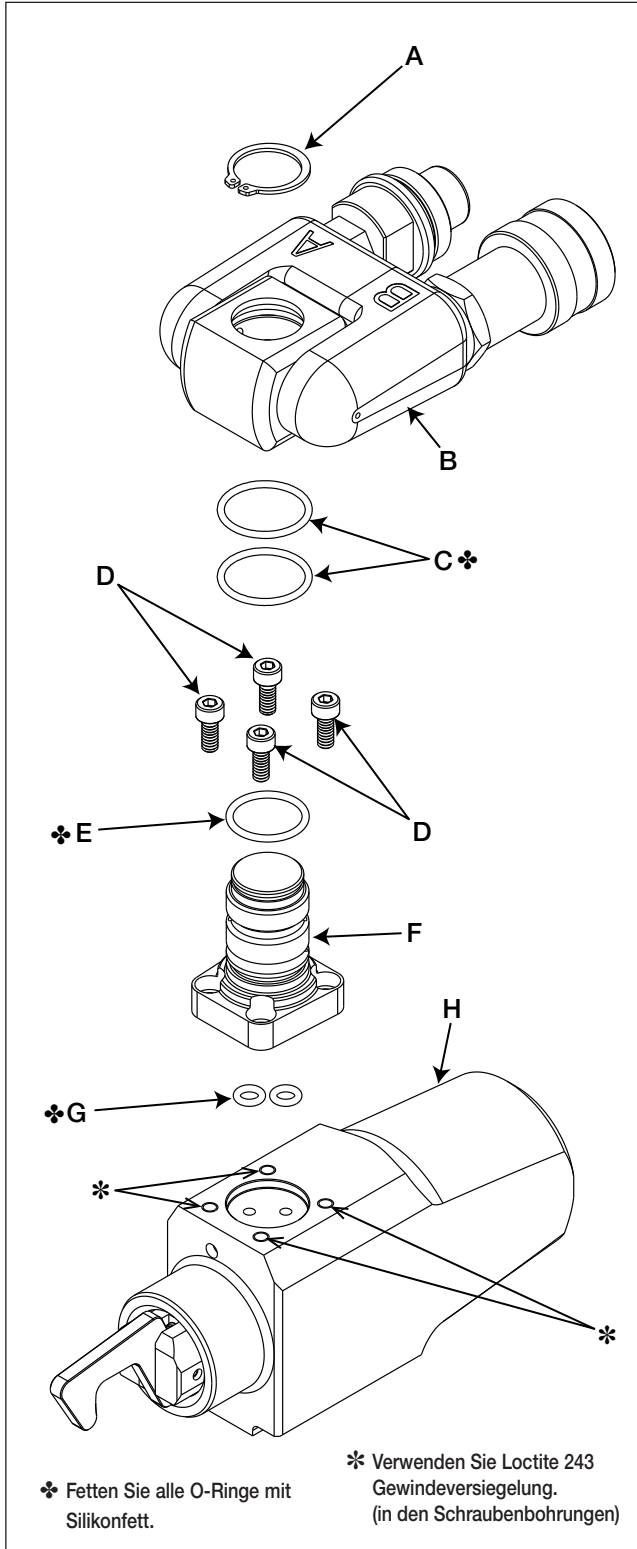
, Explosionszeichnung - Schwenkkupplung der Serie TSP300 Pro
